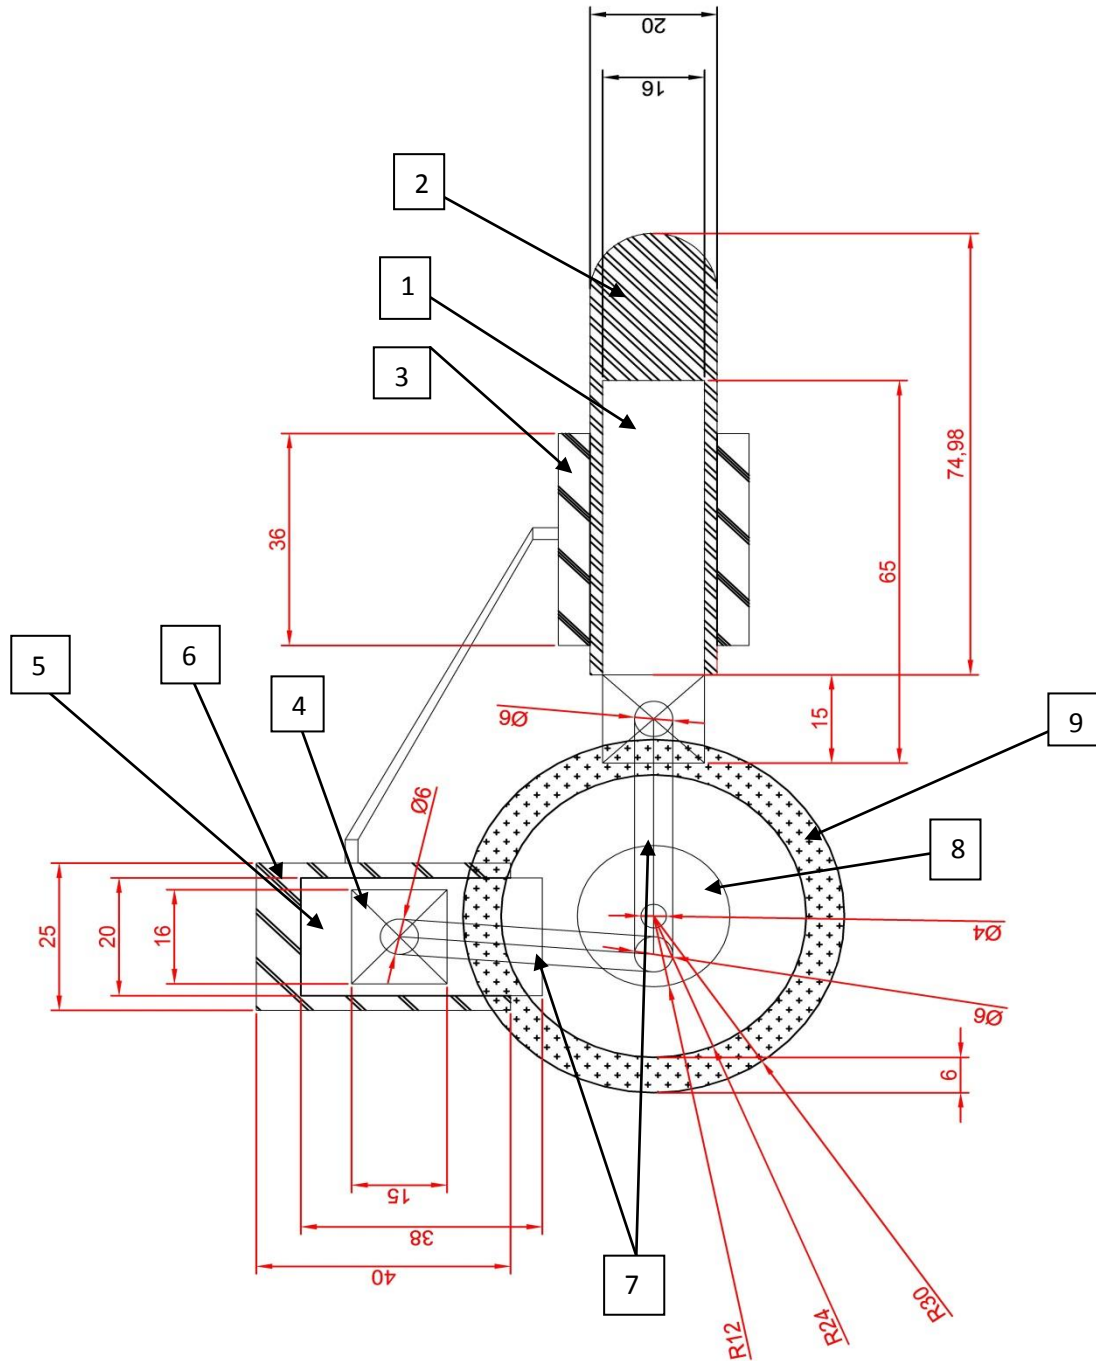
dessin d'assemblage des pièces de notre moteur (en mm)
